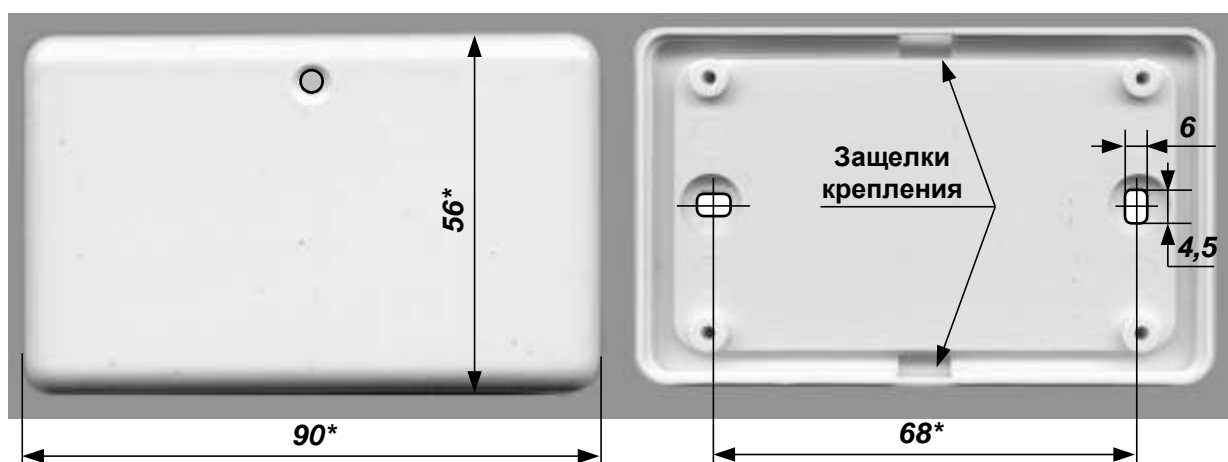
Габаритные и присоединительные размеры корпуса ИСМ
